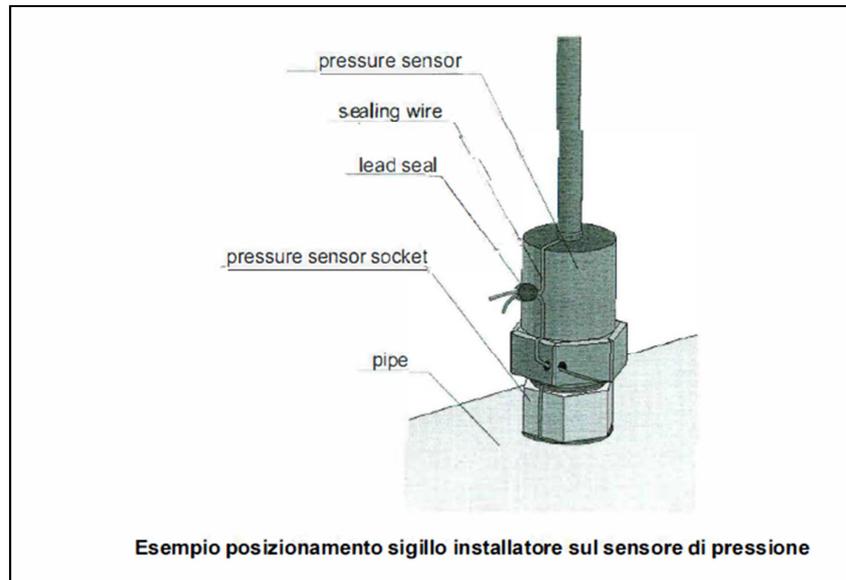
Sigillo d'installazione applicato su presa di pressione (sensore di pressione)
